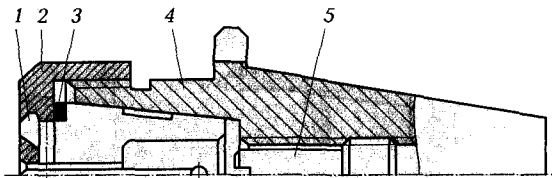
Цанговый патрон для инструмента с цилиндрическим хвостовиком:
